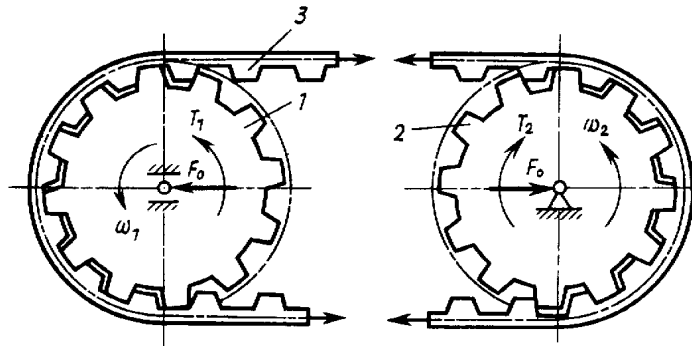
Схема зубчатоременной передачи: 1 и 2 – шкивы (звездочки); 3- ремень
